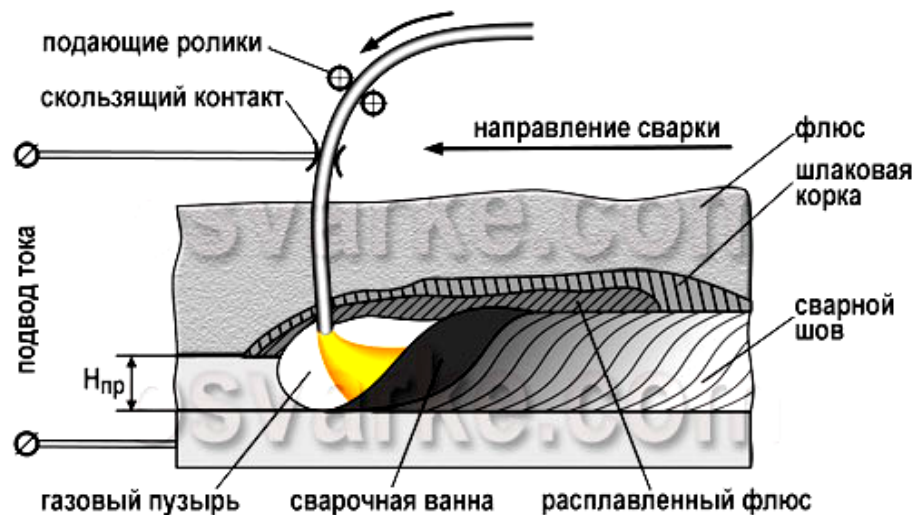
Схема дуговой сварки под флюсом
